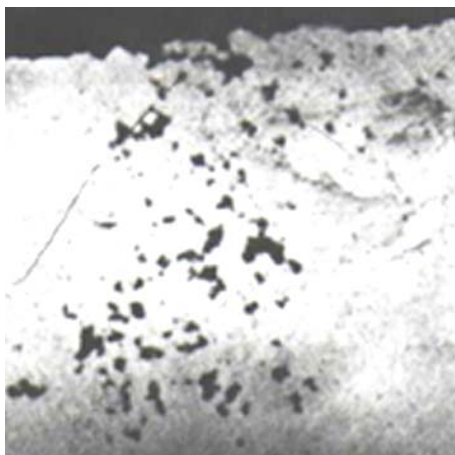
Фрагмент отливки «Гильза цилиндров» с пористостью
